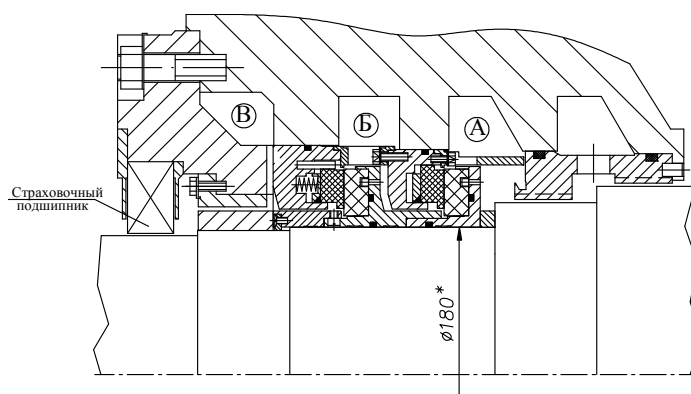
Торцовое уплотнение бесмасляных компрессоров агрегатов типа ГПА-Ц-25 и ГПА-Ц-16С. Обозначения см. на рис. 2
